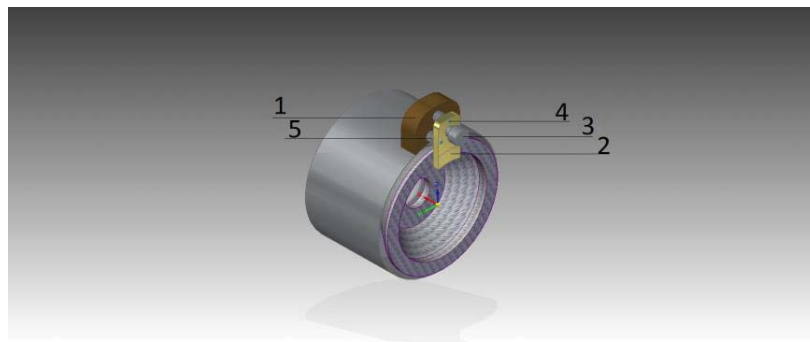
Конструкция катода для непрерывной правки алмазного круга
